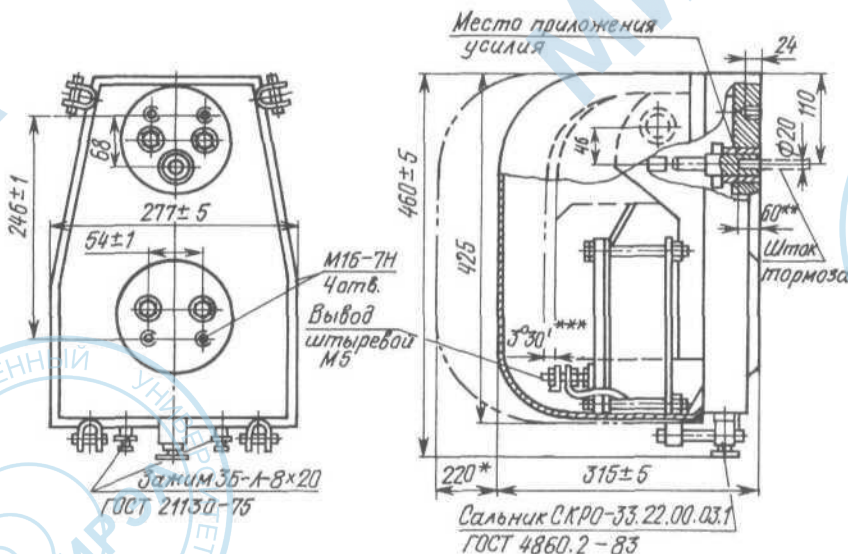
Габаритные и установочные размеры электромагнита типа MOM-310
